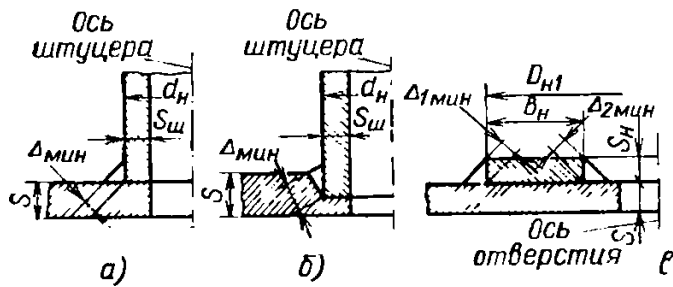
Размеры сварных швов укрепляющих элементов, принимаемые в расчетах:
